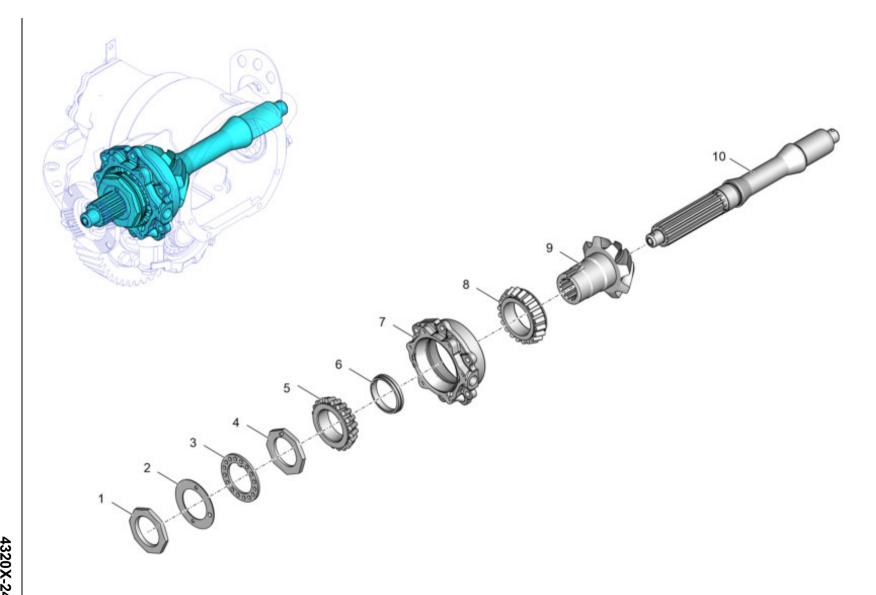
4320Х-2402005-01 Установка ведущей конической шестерни
